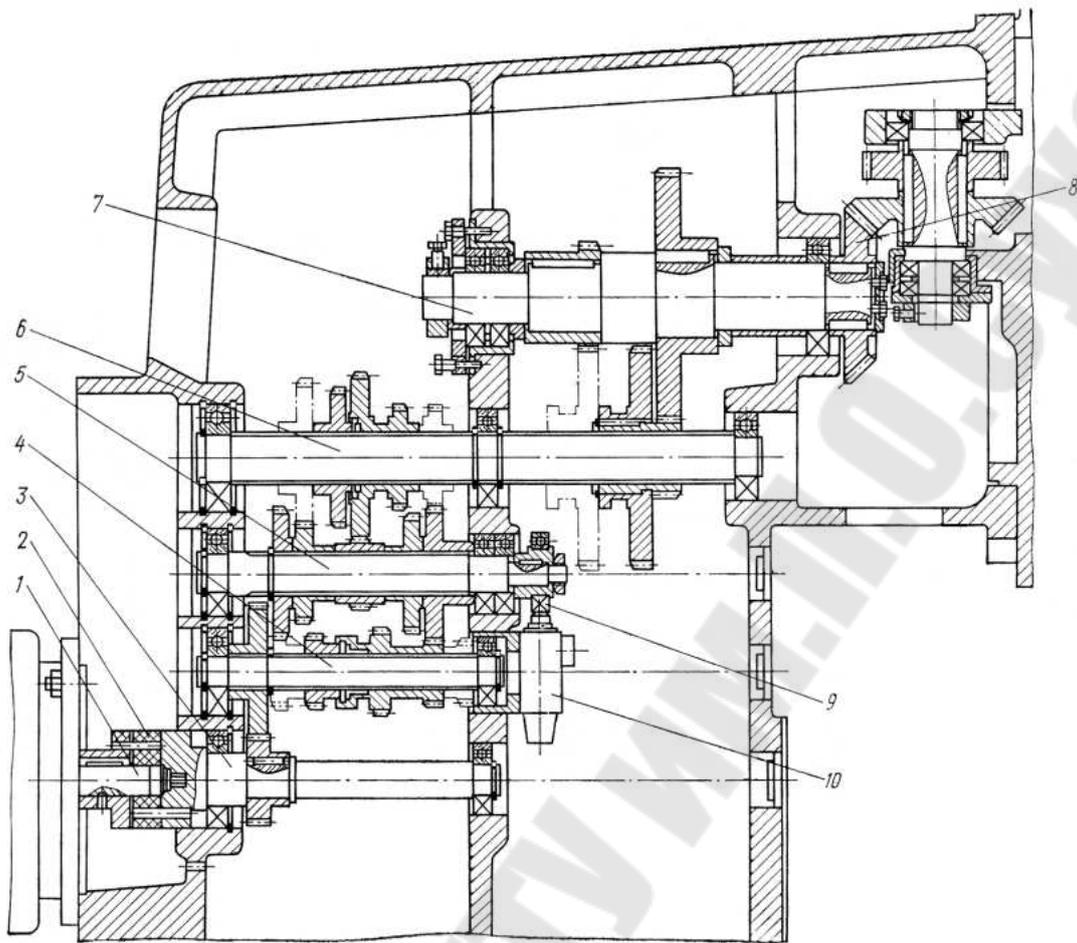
Коробка скоростей вертикально-фрезерного станка Р13Ф3-37:
